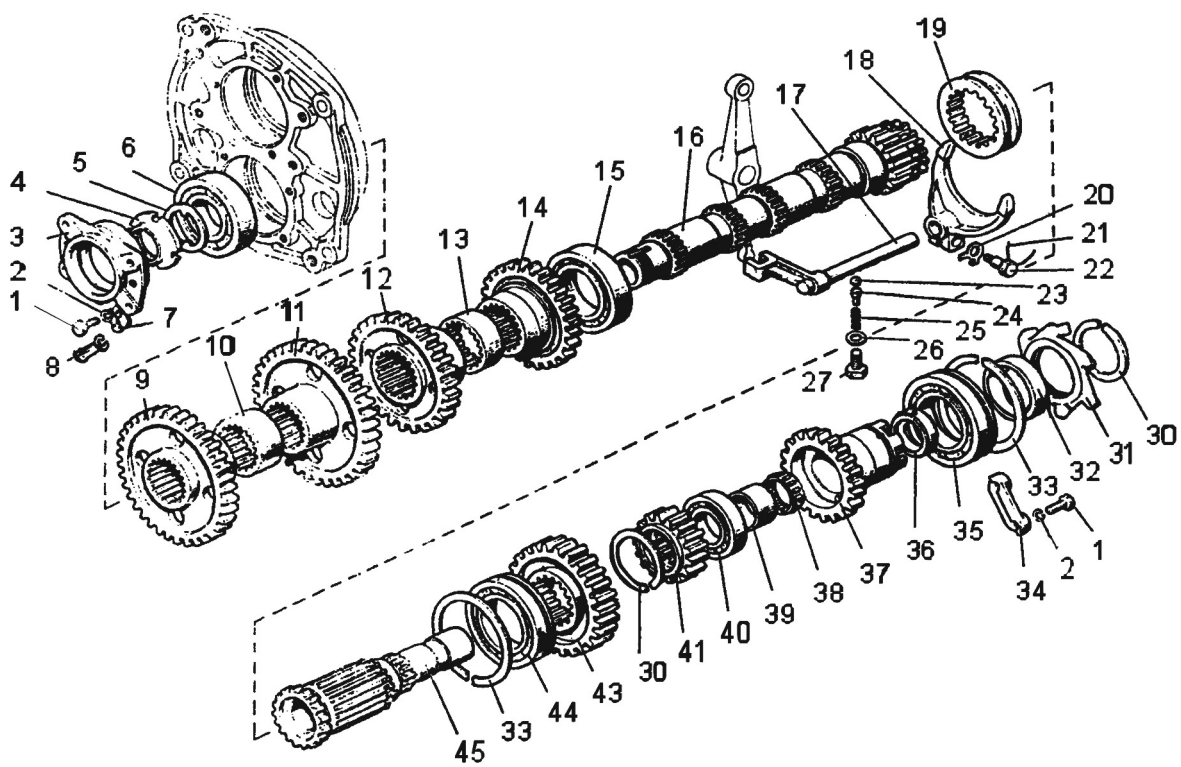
Коробка передач – Вал промежуточный. Шестерня
